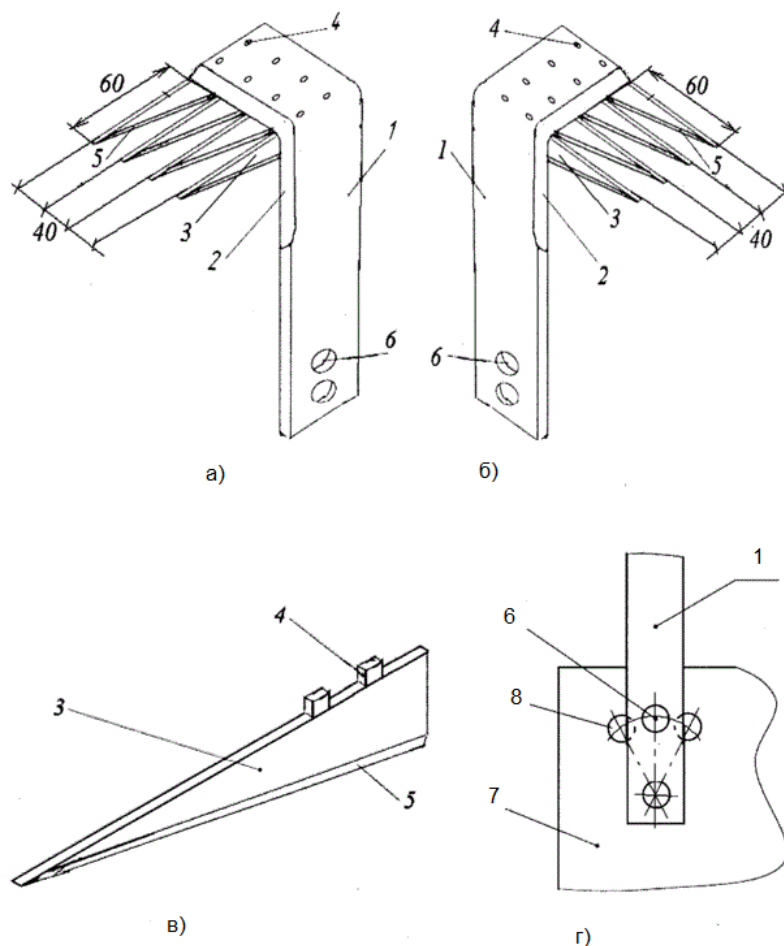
Схема ножа почвообрабатывающей фрезы
